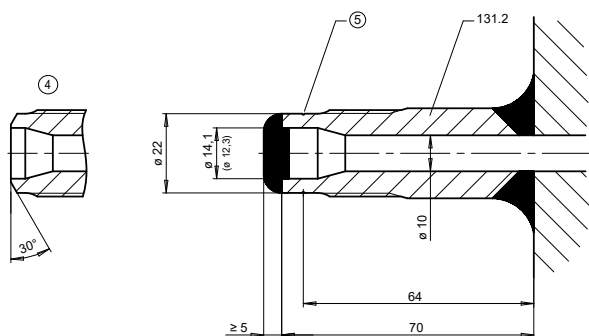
Закрытый патрубок для защиты от избыточного давления
